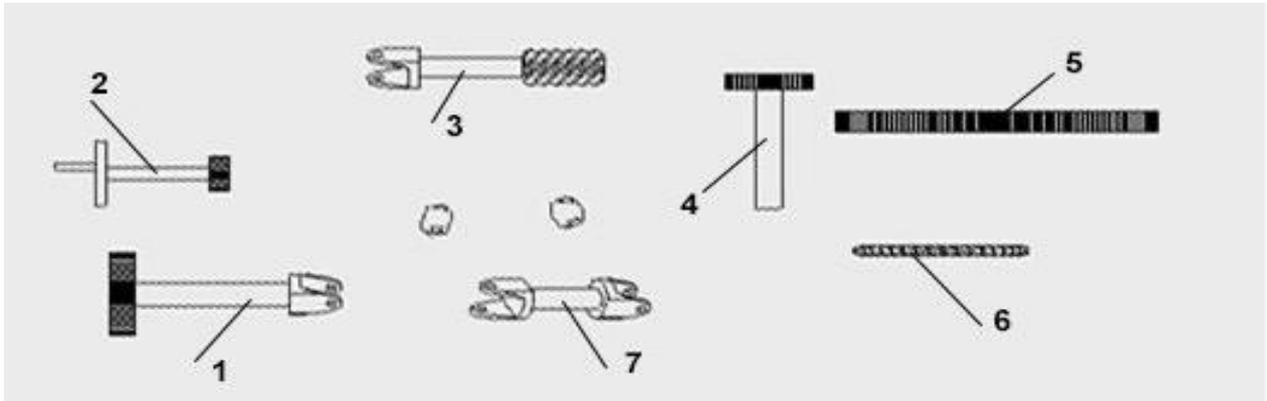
Початкове положення складових механізму наведення: 1,4 – вал з шестернею; 2 – маховик з шестернею; 3 – черв'як; 5 – зубчатий сектор; 6 – черв'ячне колесо; 7 – шарнір;
